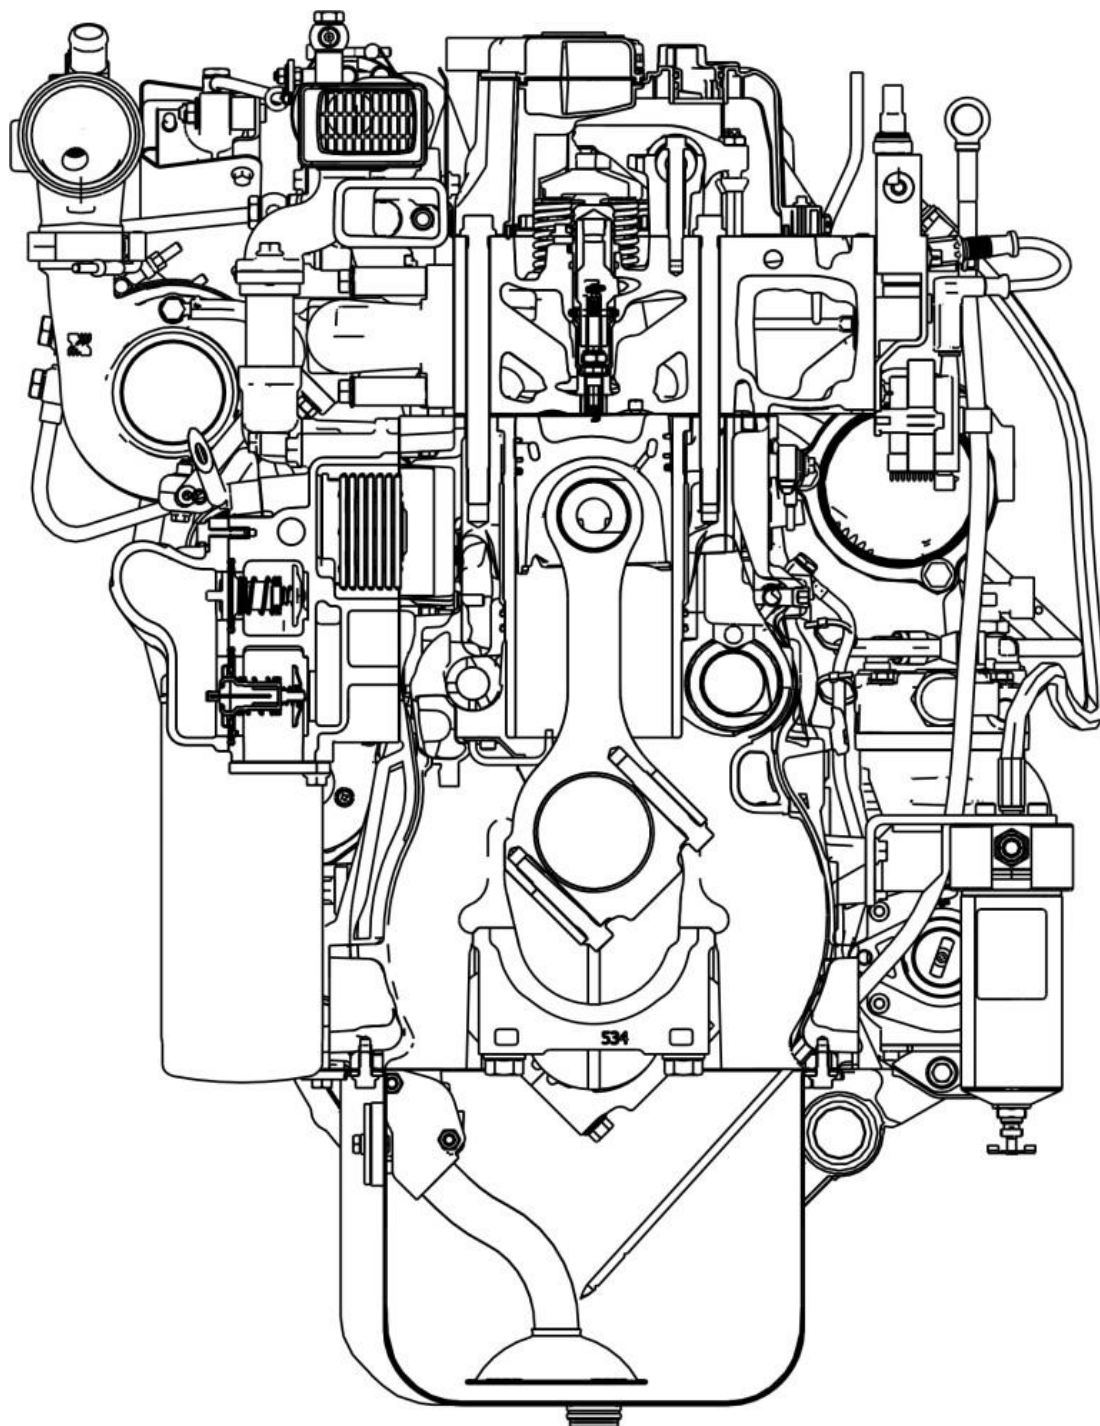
Поперечный разрез двигателя ЯМЗ-53414
